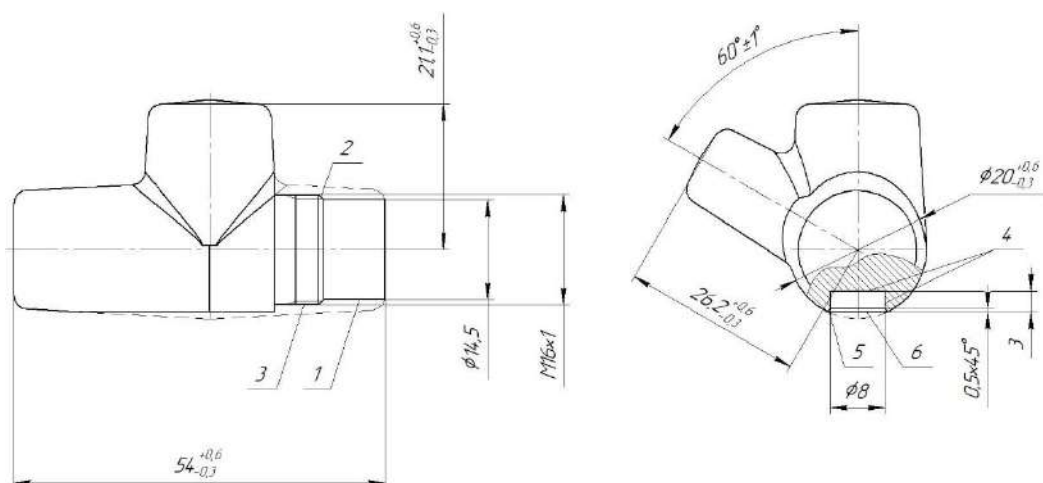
Проміжна заготовка корпусу Р30.00.921 з позначенням нумерації поверхонь, оброблених на першому етапі (підготовча обробка корпусу перед складальною операцією)
